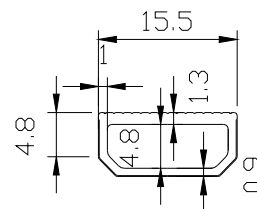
Querschnitt des Abstandhalters Thermix TX.N
